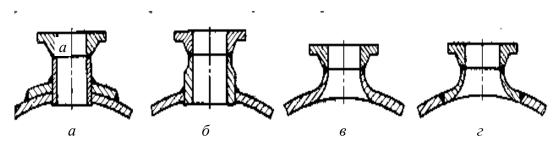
Способы соединения люков и штуцеров с корпусами аппаратов
